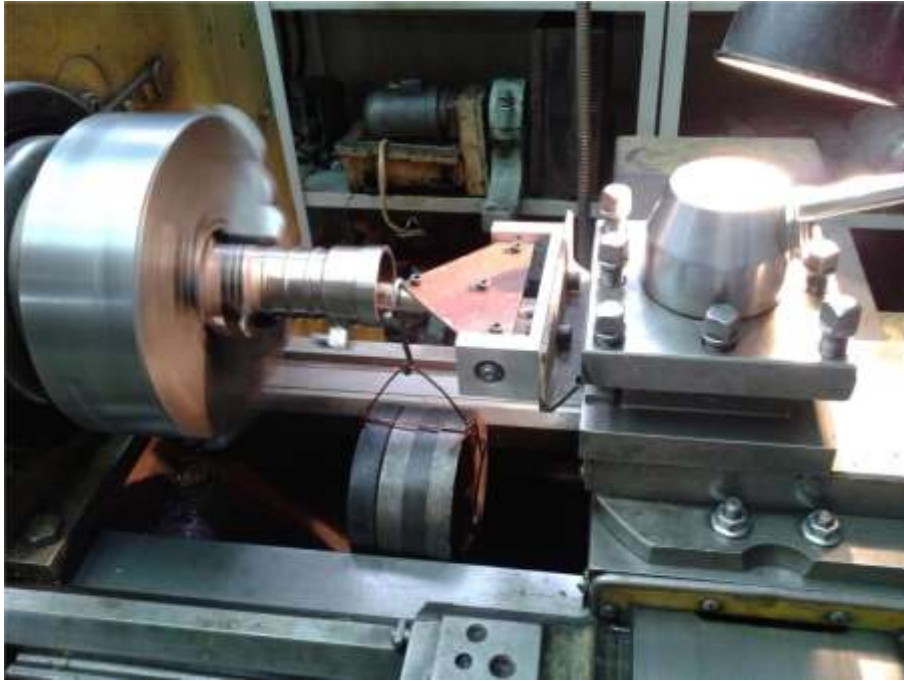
Приспособление с самоустанавливающейся державкой алмазного индентора для выглаживания цилиндра на токарном станке
